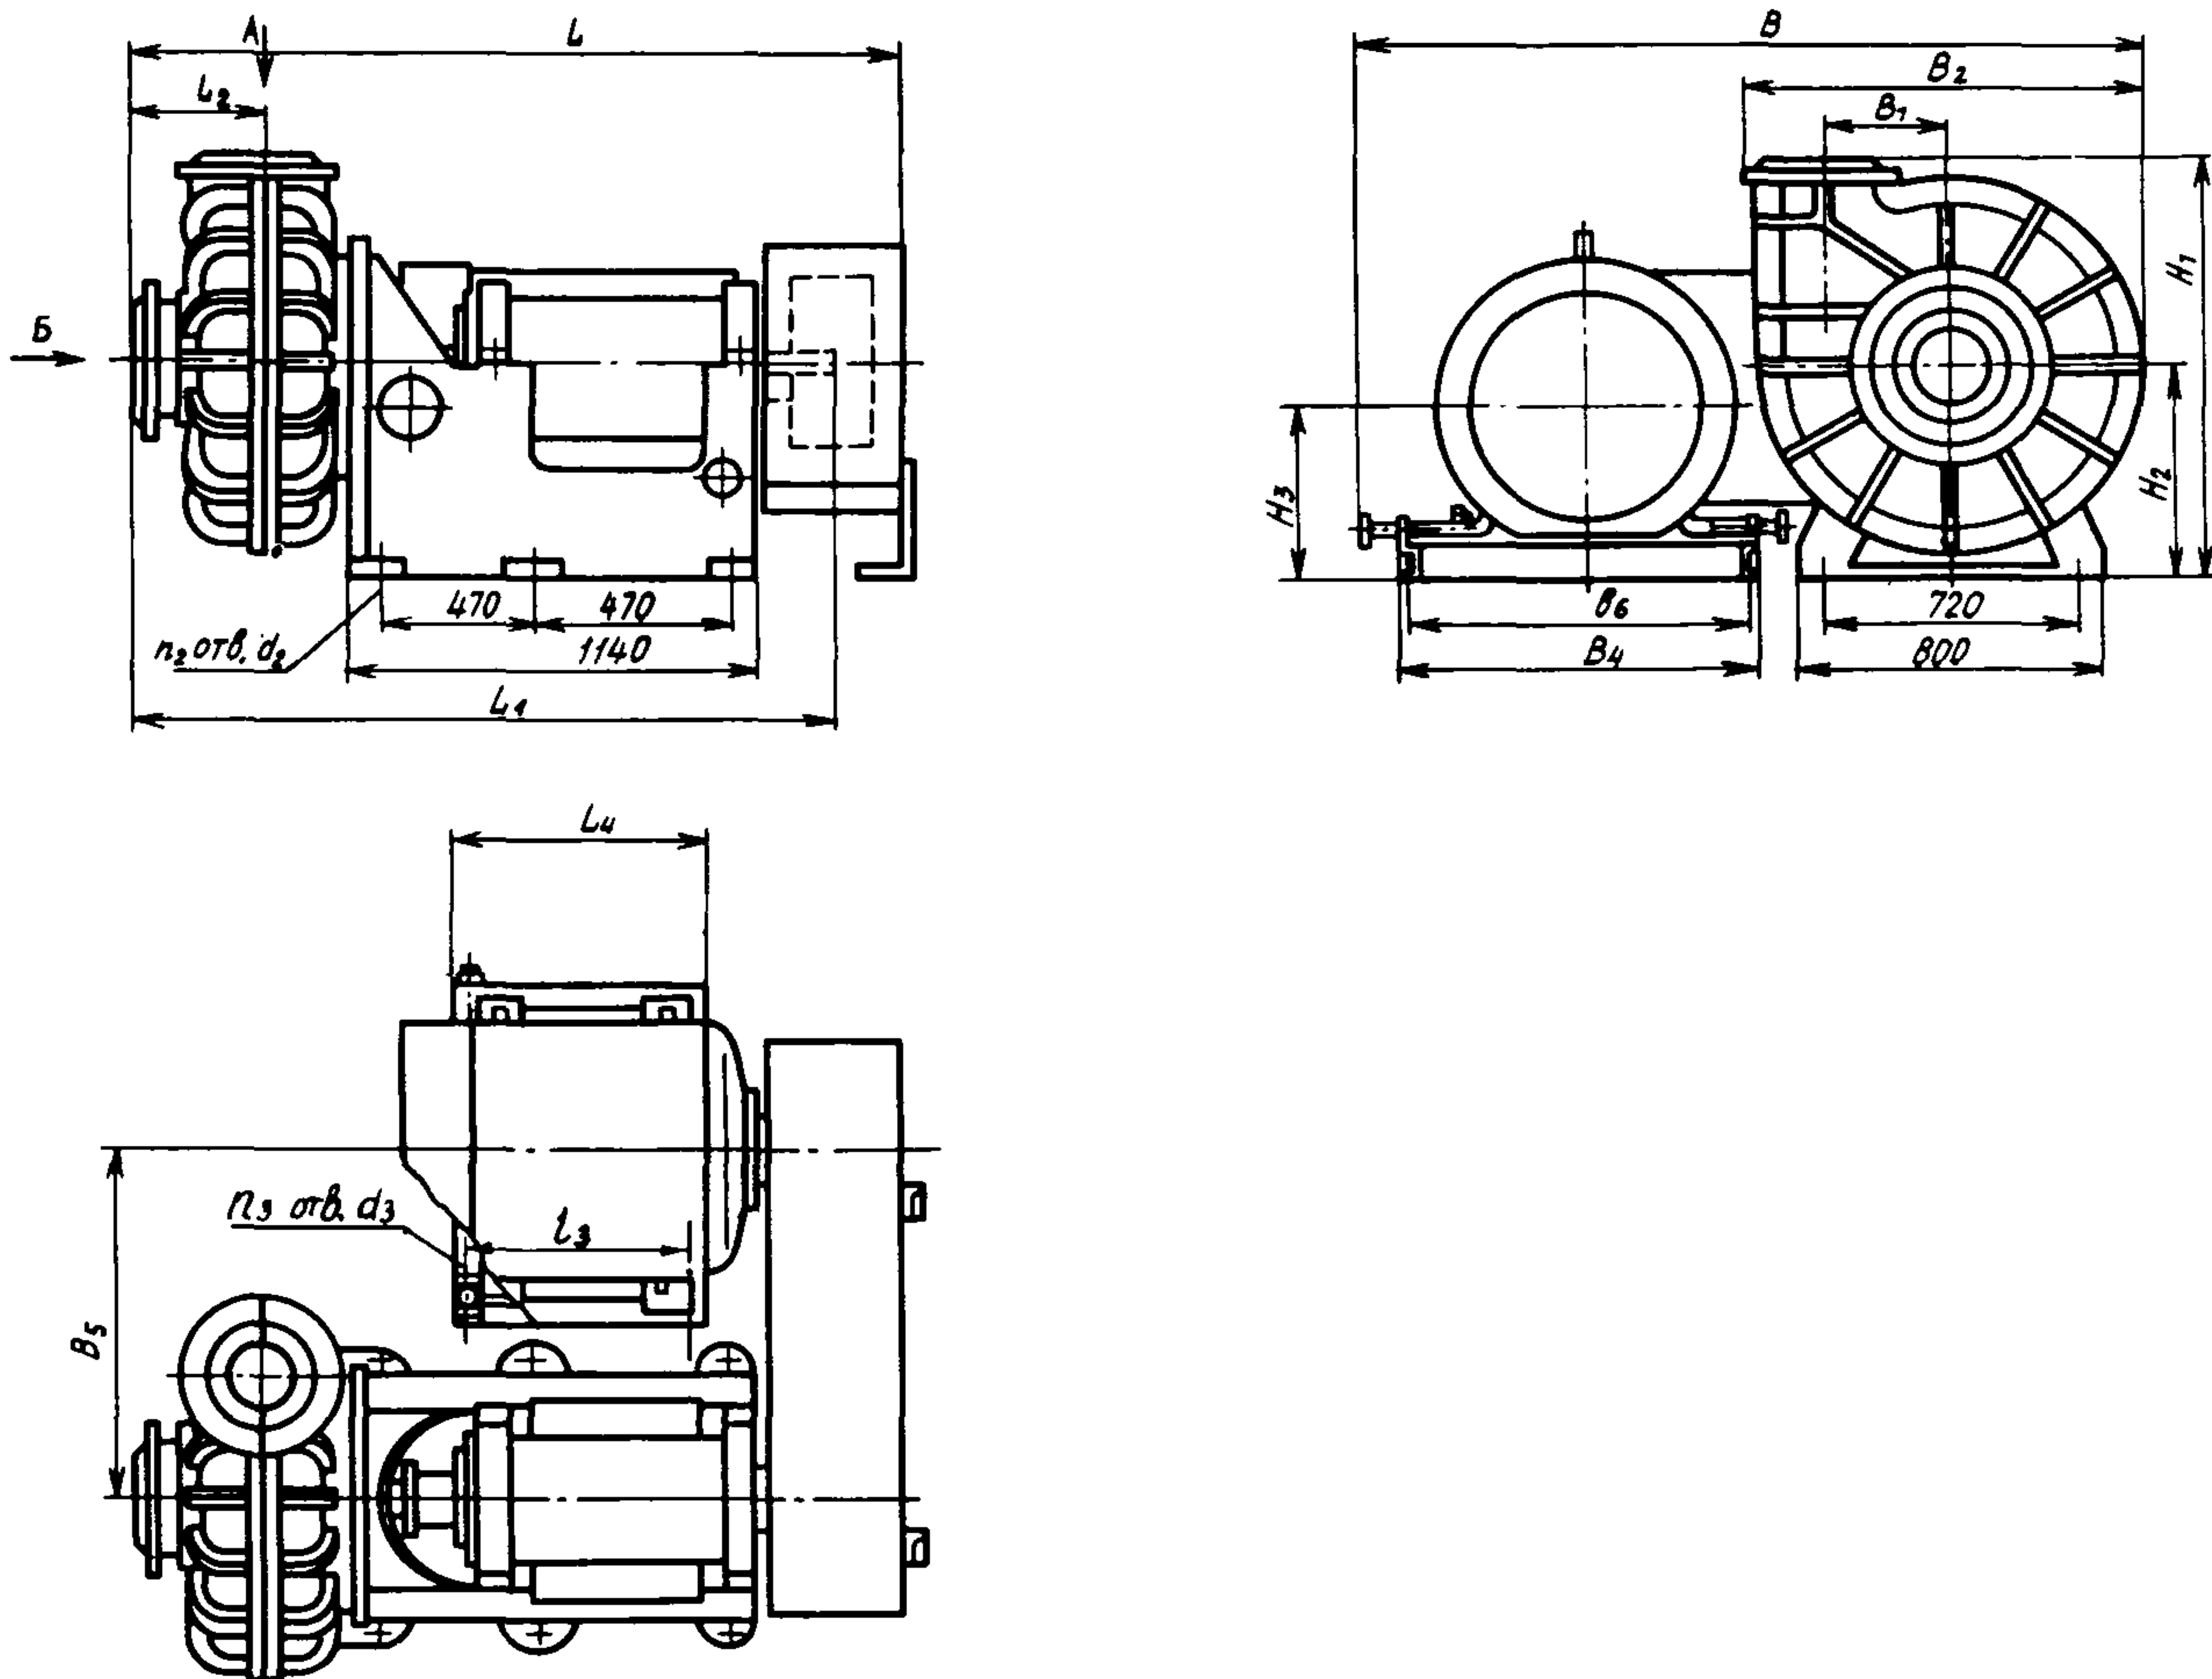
Габаритный чертеж электронасосного агрегата типа ГрА с приводом через клиноременную передачу (боковое расположение электродвигателя)
